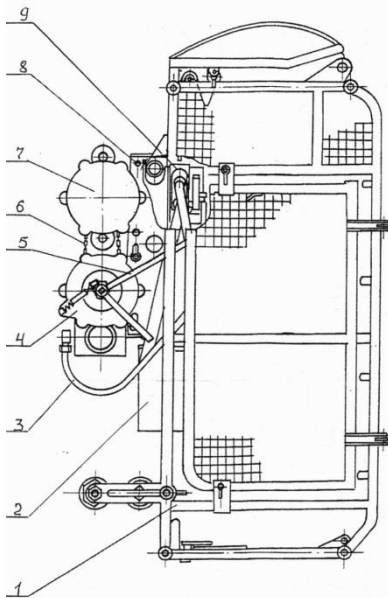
Конструкція кліті малогабаритного монорейкового аварійно-рятувального підйомника ПГР-350: 1 - кабіна; 2 - ящик інструментальний; 3 - рукав; 4 - ходова частина; 5 - планетарно-циліндричний редуктор; 6 - ланцюг; 7 - автоматичний вловлювач; 8 - рама; 9 - пульт керування
